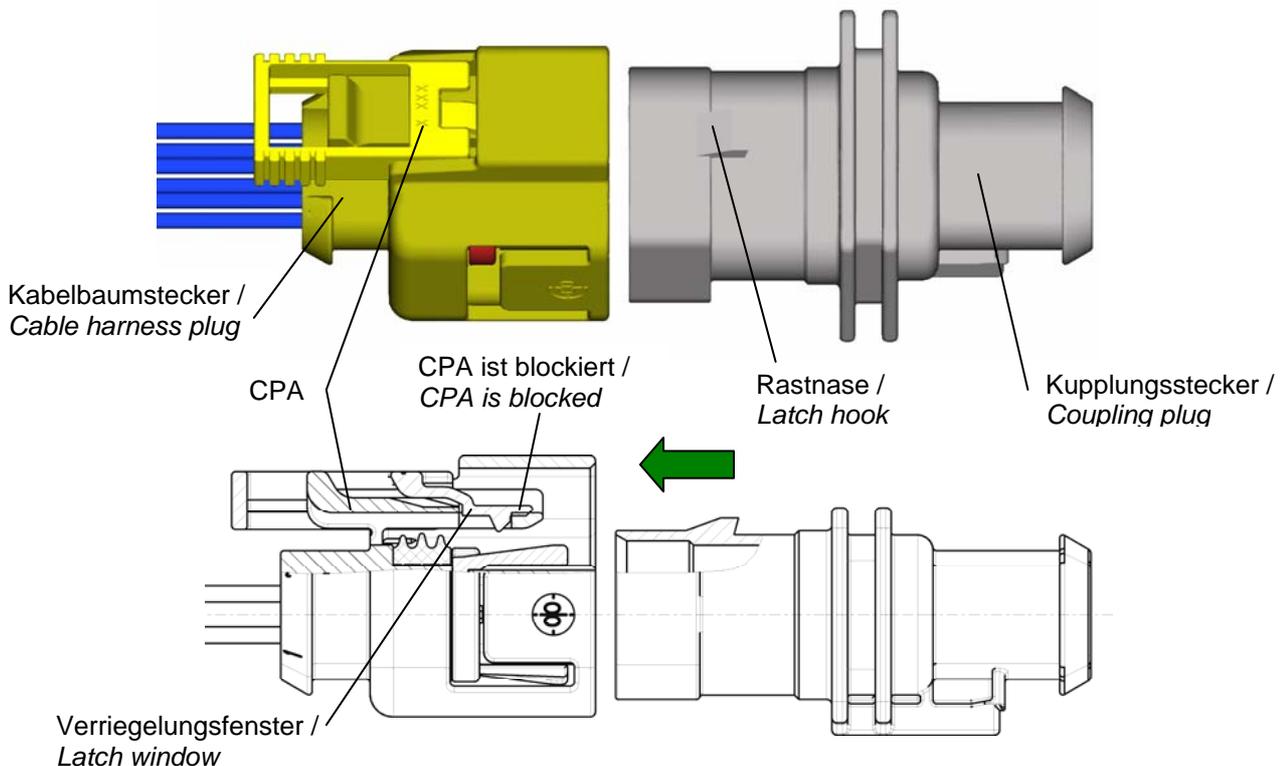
Montage Steckverbindung / Fig. 4.1.1 Assembly of the plug connection
